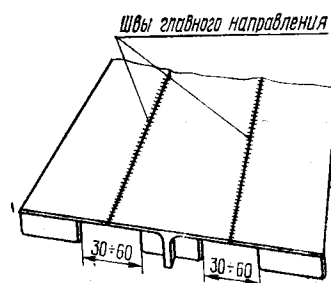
Пример конструктивного оформления сварного соединения панелей, обеспечивающего применение сварочного автомата.
